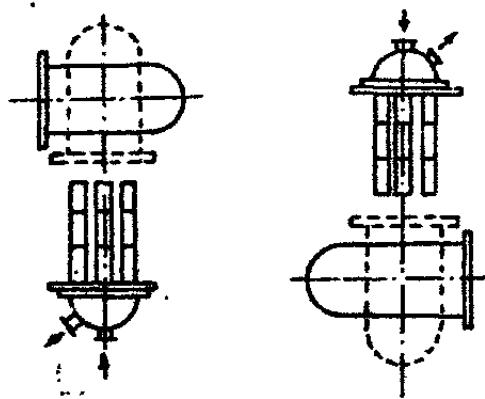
Схема возможных вариантов положения фильтра и съемного корпуса: 1 — корпус сдвигается вверх с поворотом; 2 — корпус сдвигается вниз с поворотом [31]
